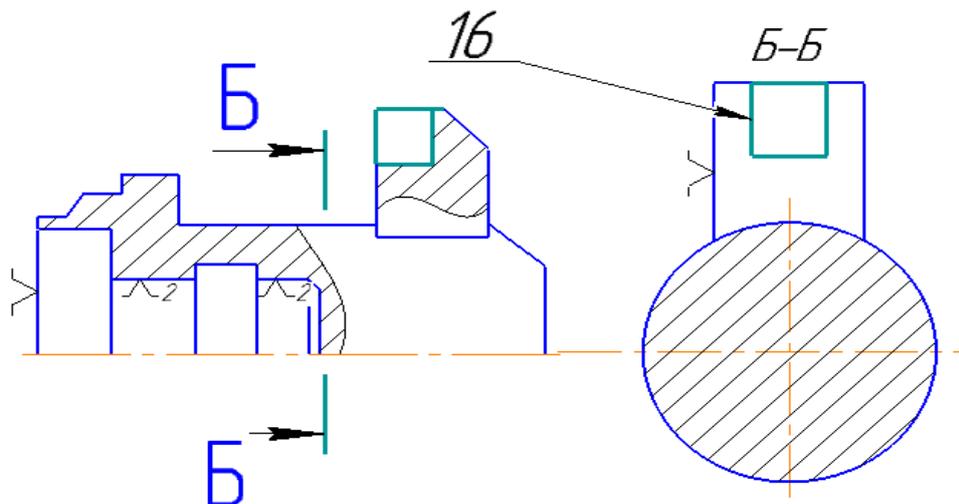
Эскиз фрезерной операции с ЧПУ 015, установ Б
